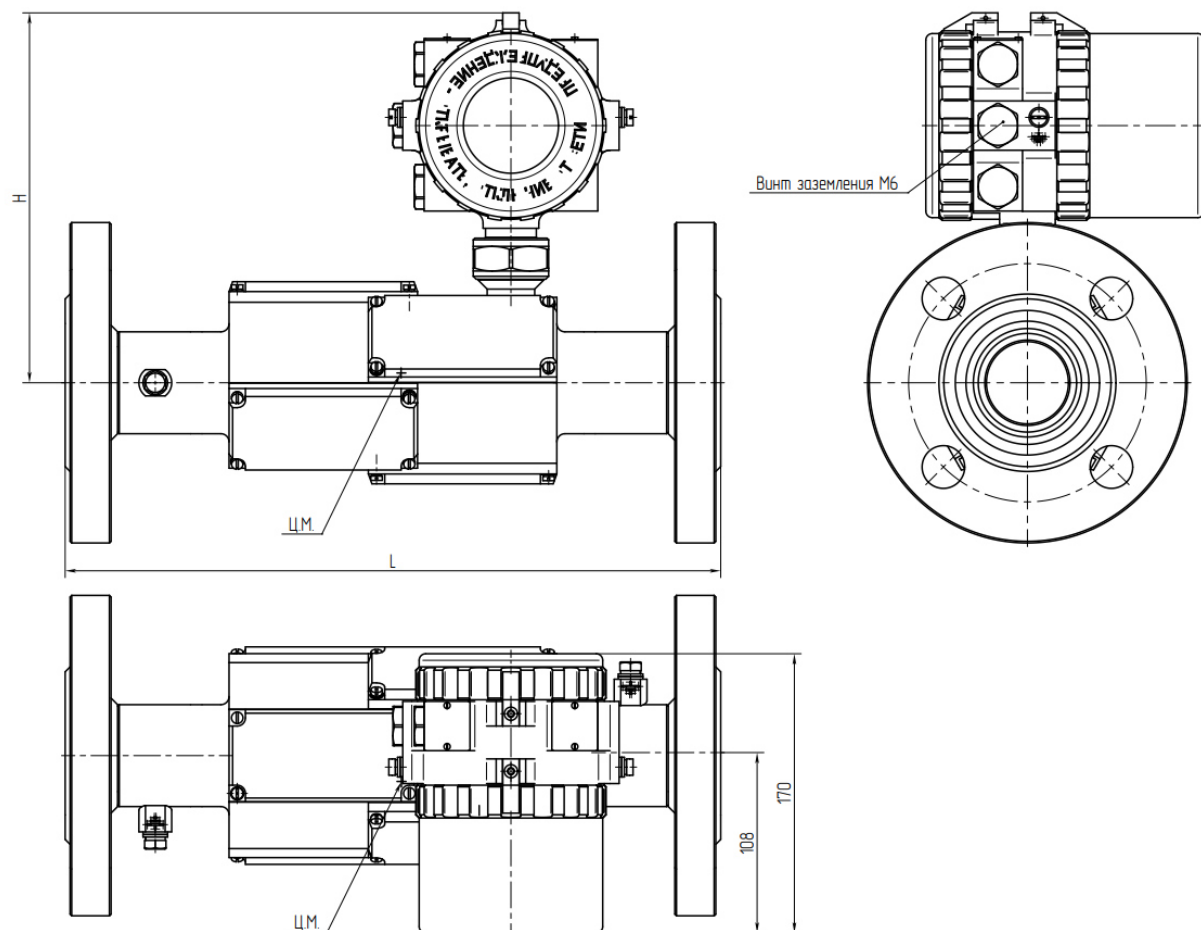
Габаритные и установочные размеры расходомера одноблочного исполнения DN50...80 (таблица Д.5)
